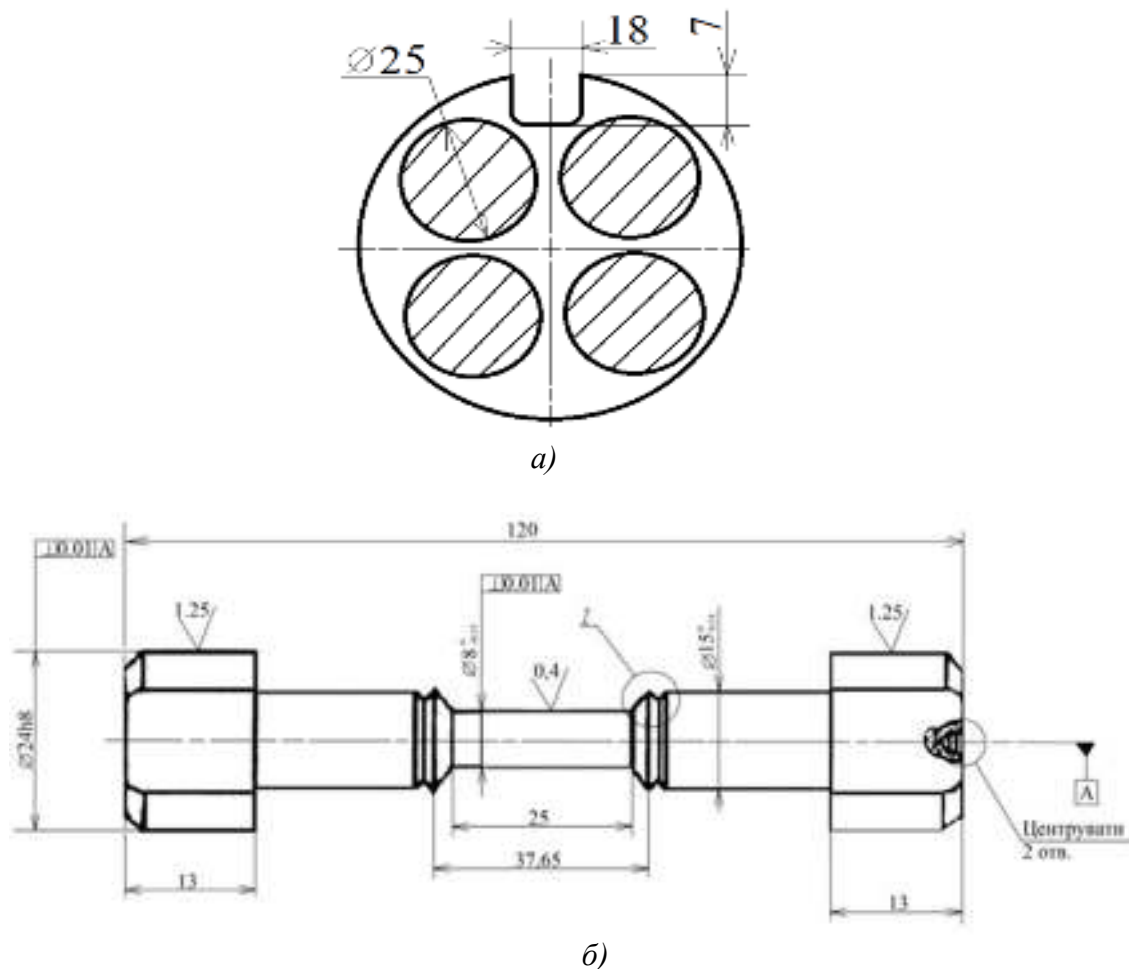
Схема вирізання заготовок для виготовлення зразків (а) та зразок з металу хвостовика вала якоря генератора DUGG-28 для випробувань на крутіння (б)
